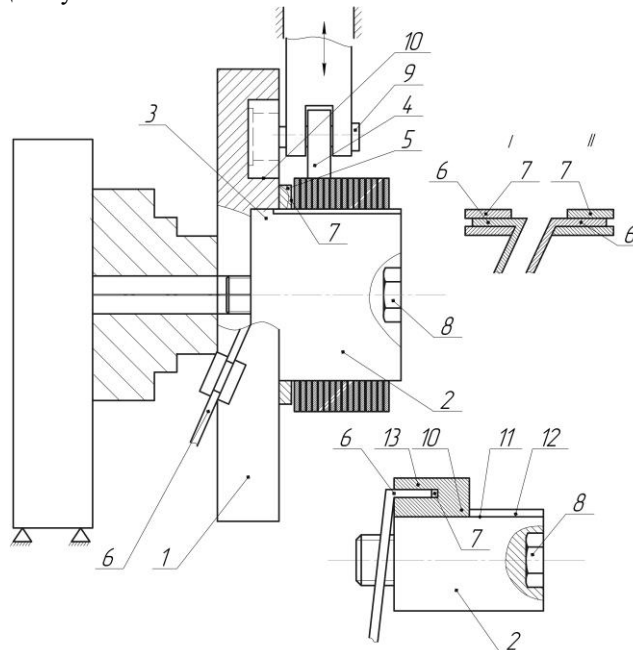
Універсальний пристрій для виготовлення гвинтових заготовок різного профілю
